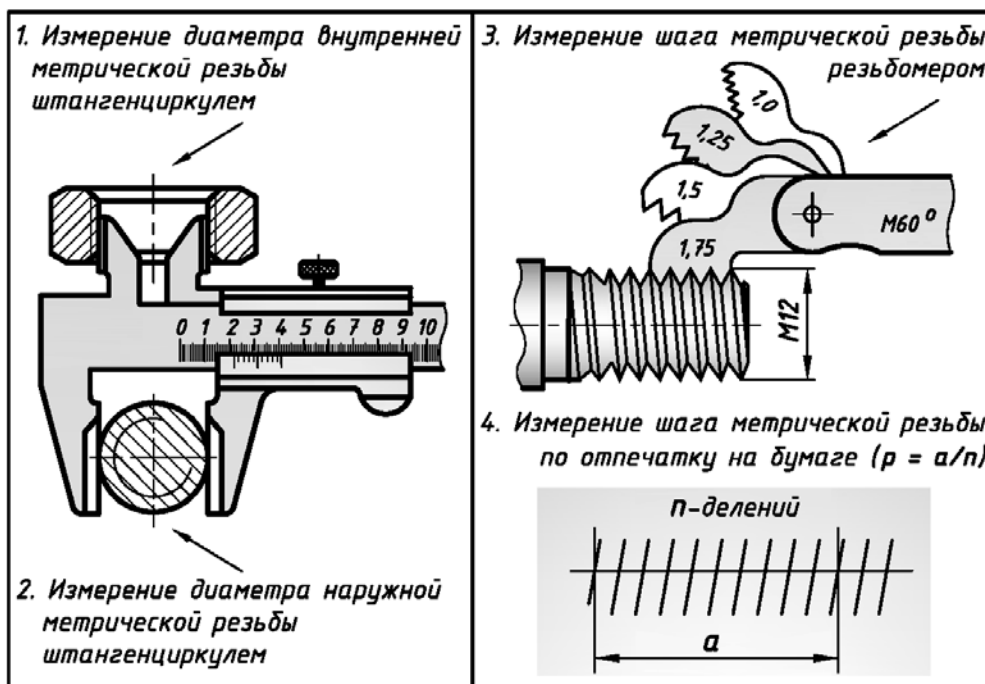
Определение параметров резьбы метрической цилиндрической
